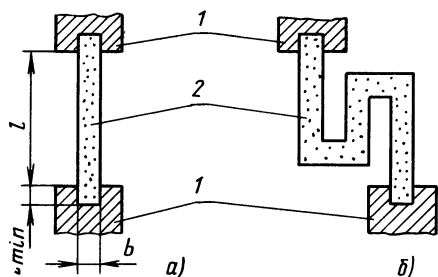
Конструкция пленочного резистора: а — линейного; б — криволинейного; 1 — проводящая пленка; 2 — резистивная пленка
